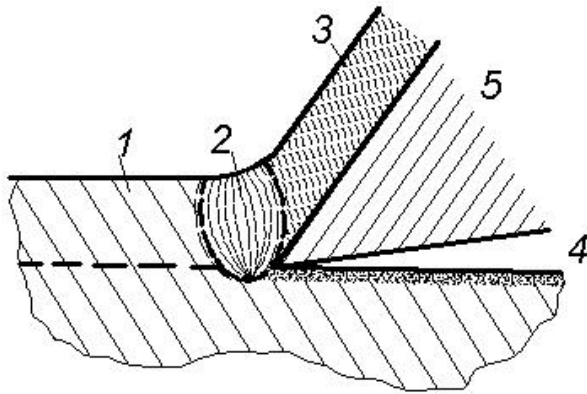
Утворення деформованого шару при різанні пластичного металу: 1 – основна структура металу; 2 – зона пластичної деформації; 3 – стружка; 4 – пластично деформований поверхневий шар; 5 – інструмент
